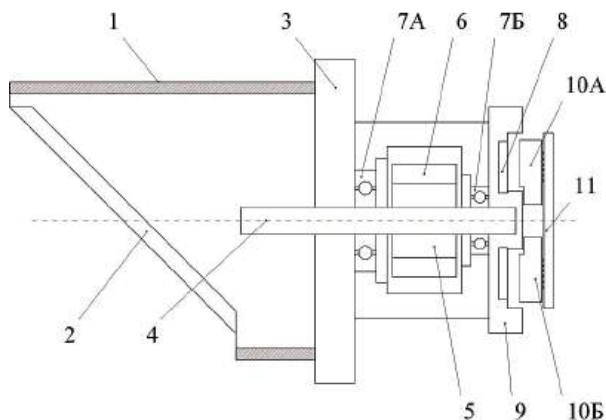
Конструкция привода отклоняющего устройства сканера FARO: 1 — держатель; 2 — отклоняющее зеркало; 3 — кольцевой диск; 4 — вал; 5 — ротор электродвигателя; 6 — статор электродвигателя; 7А, 7Б — пары подшипников; 8 — энкодер; 9 — корпус; 10А, 10Б — считывающие головки; 11 — печатная плата управления
